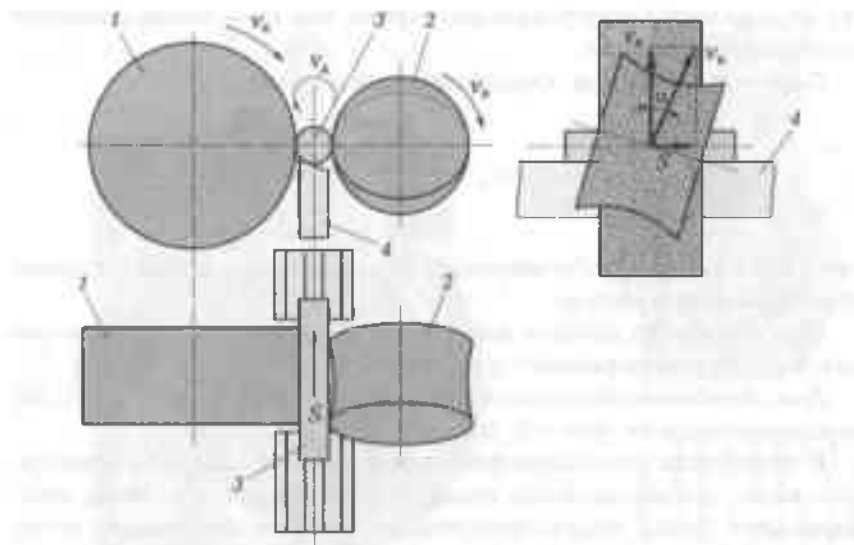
Схема устройства бесцентрового круглого шлифования:
